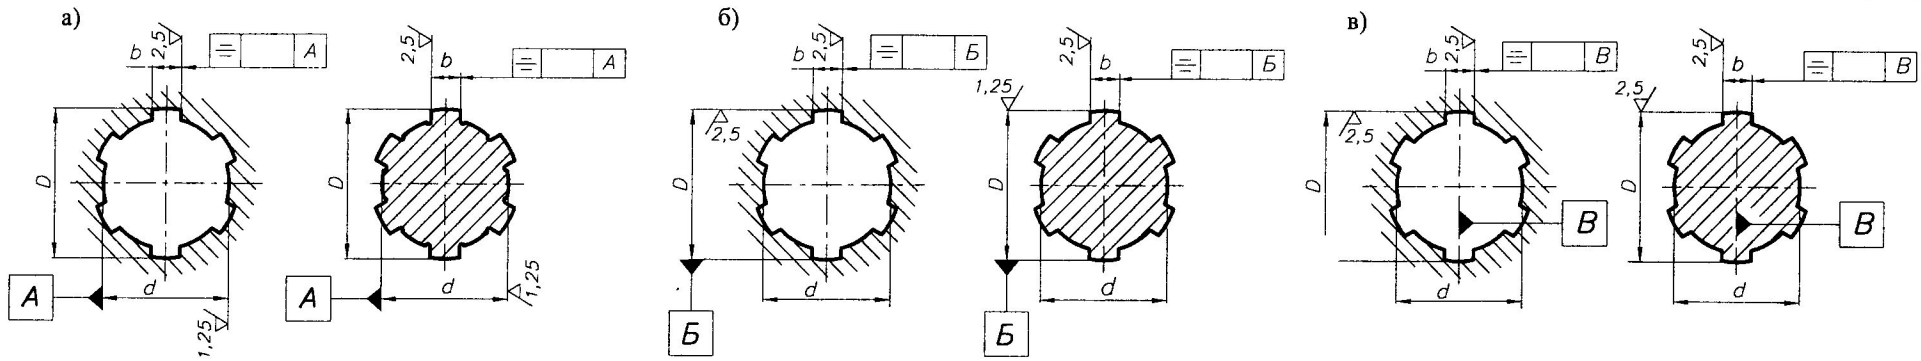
Базовые поверхности, чистота обработки и допуски формы и расположения поверхностей шлицевого прямобочного соединения при центрировании: а) по d ; б) по D ; в) по b
